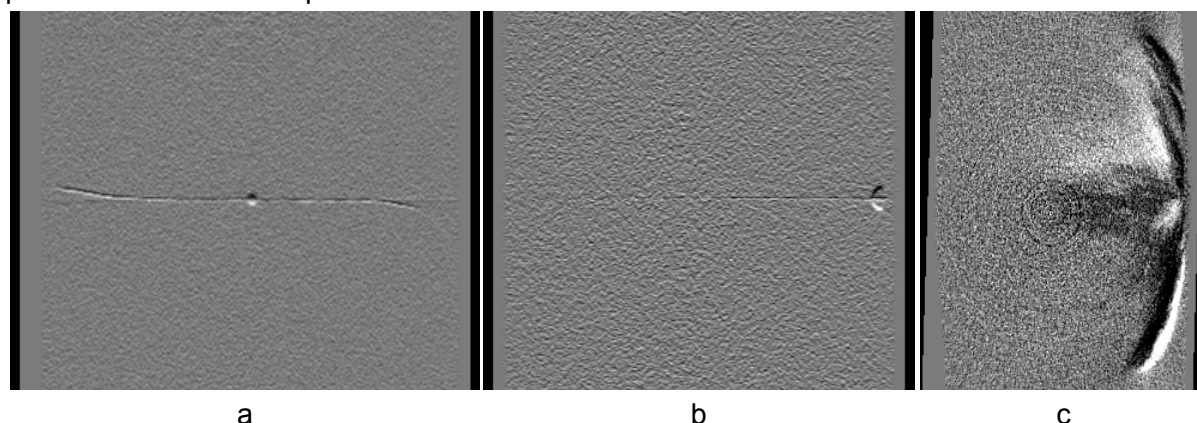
Projections d'une reconstruction tomographique effectuée sur éprouvette à défaut hémisphérique en fin de fissuration sollicitée sous rapport de charge -1 : (a) vue de face, (b) vue en coupe de côté et (c) vue en coupe de la section utile au niveau de la fissure
